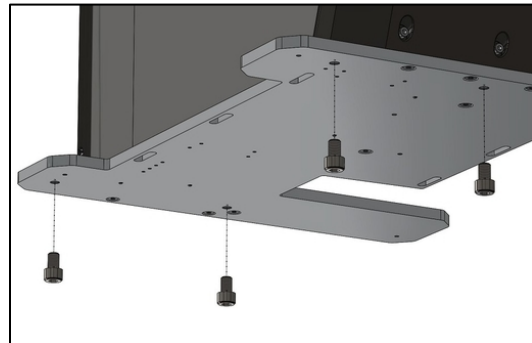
Pour fixer la machine sur un support ou bâti, utilisez une clé à six pans de 6 mm.
